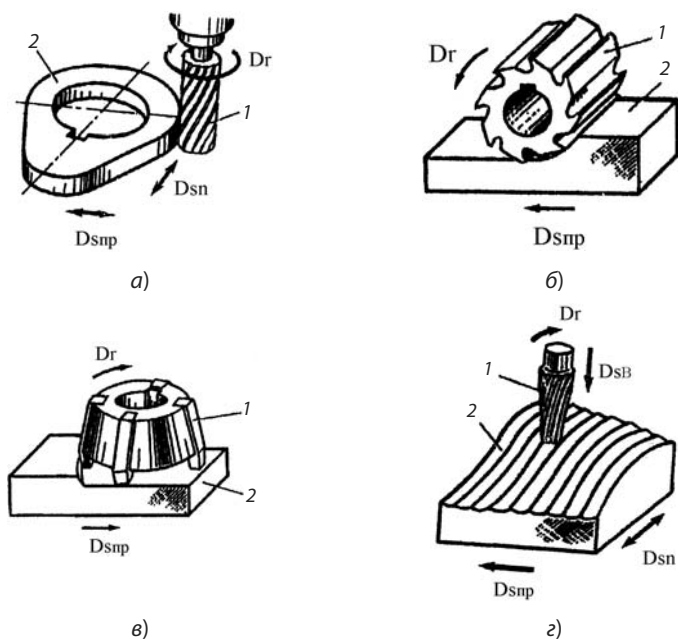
Схемы формообразования поверхностей фрезерованием:
